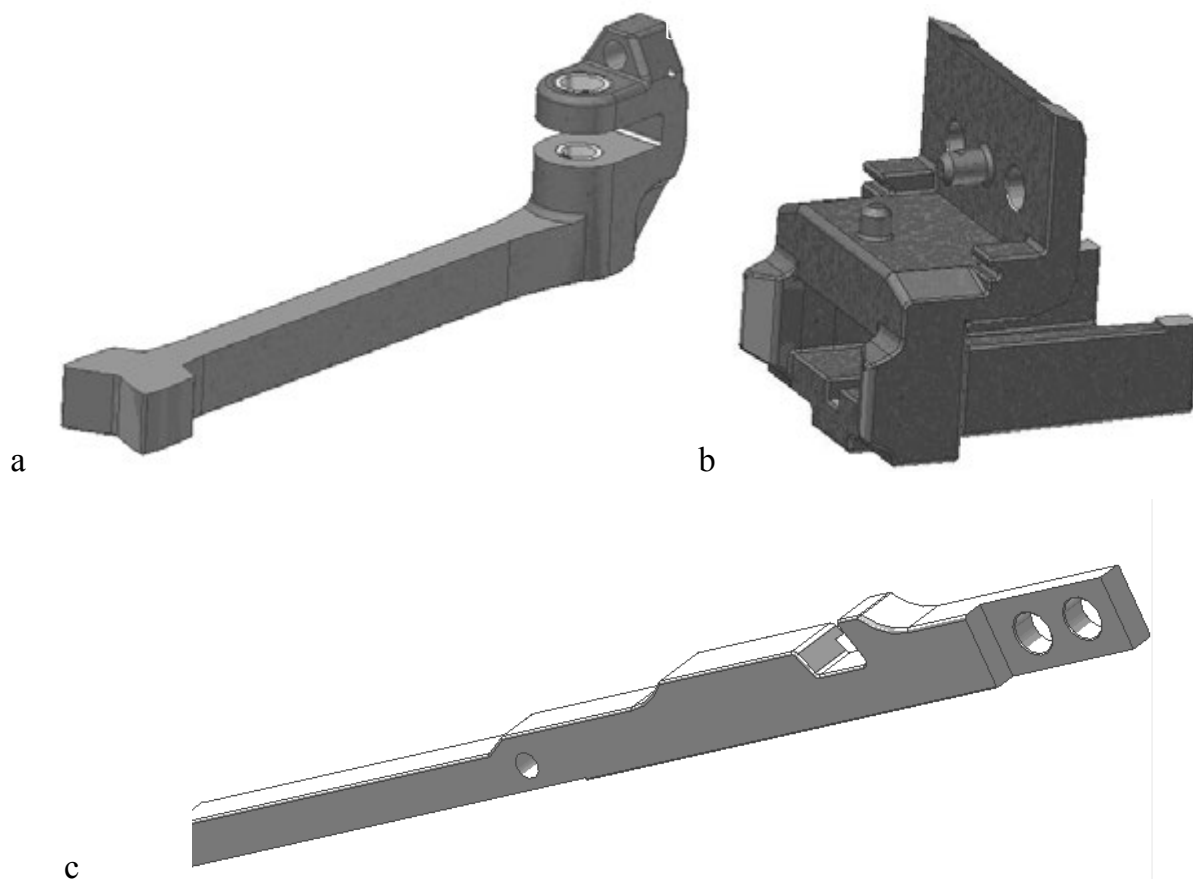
Составные части замыкателя стрелочного перевода: а) кляммер; б) скобообразный корпус (направляющая); с) ведущая штанга (ползун)
